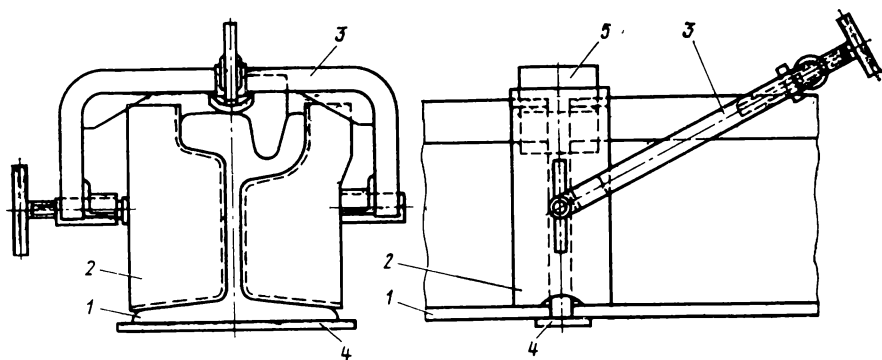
Схема сборной ванны при электродуговой сварке ванным способом:
